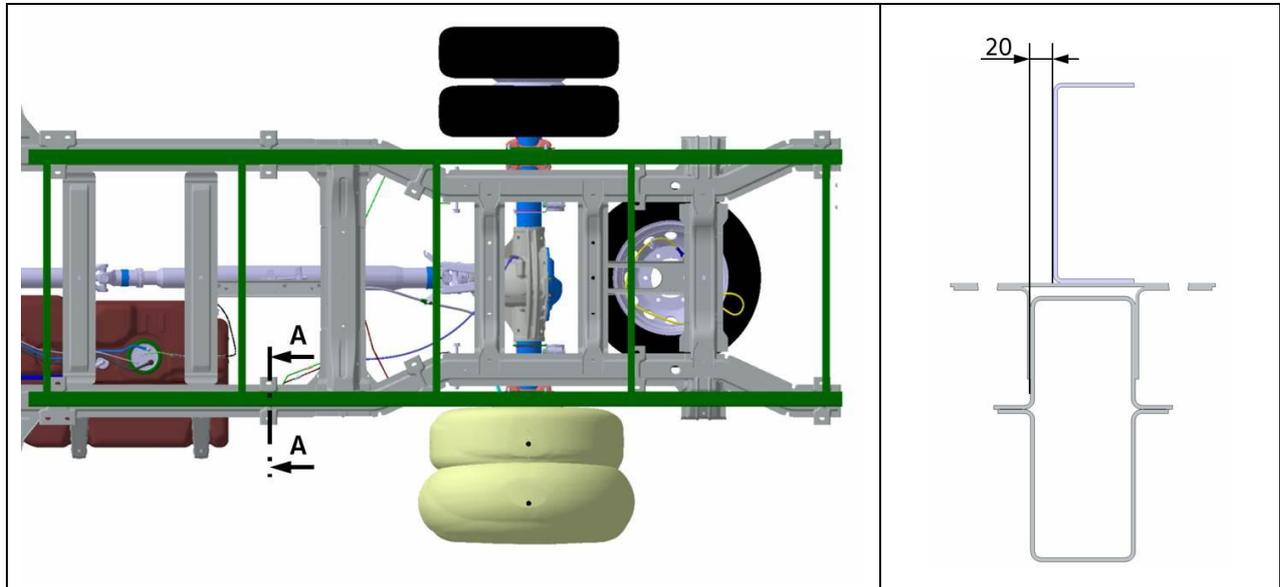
Décalage du cadre de montage pour les cadres coudés
